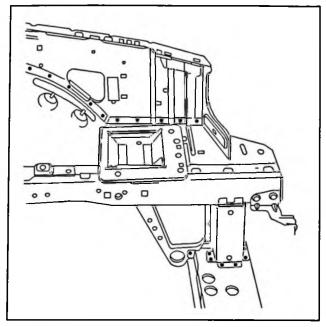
AP02QC Souder par points électriques. Souder par points "bouchon" MAG.
